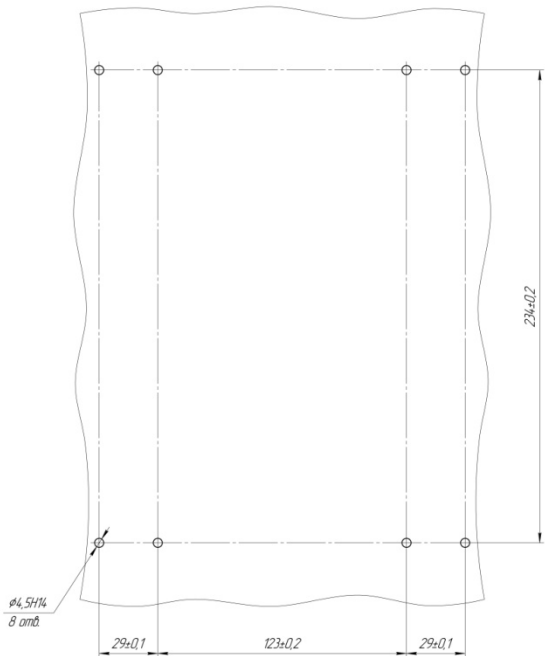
Габаритные и присоединительные размеры устройства РС830-ДТ2 при внешнем монтаже, обеспечивающем его поворот вверх/вниз
